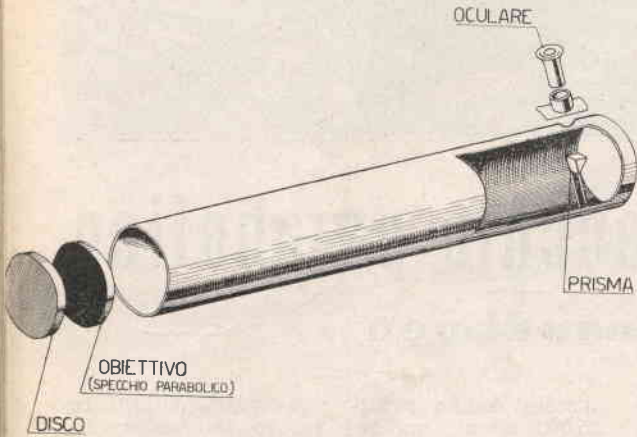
Schema montaggio parte ottica. - Sulla parte posteriore del tubo appare lo specchio parabolico montato sopra un disco di legno, il quale ultimo risulta solidale al tubo stesso mediante vite di presa laterale.
